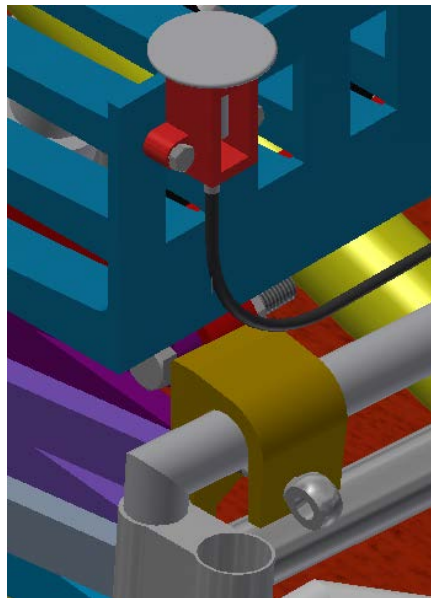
Anclaje del mecanismo en el marco de la silla de ruedas.
